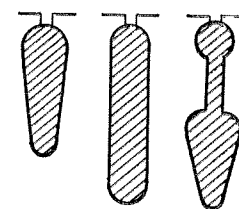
Формы пазов роторов двигателей с заливкой алюминием
